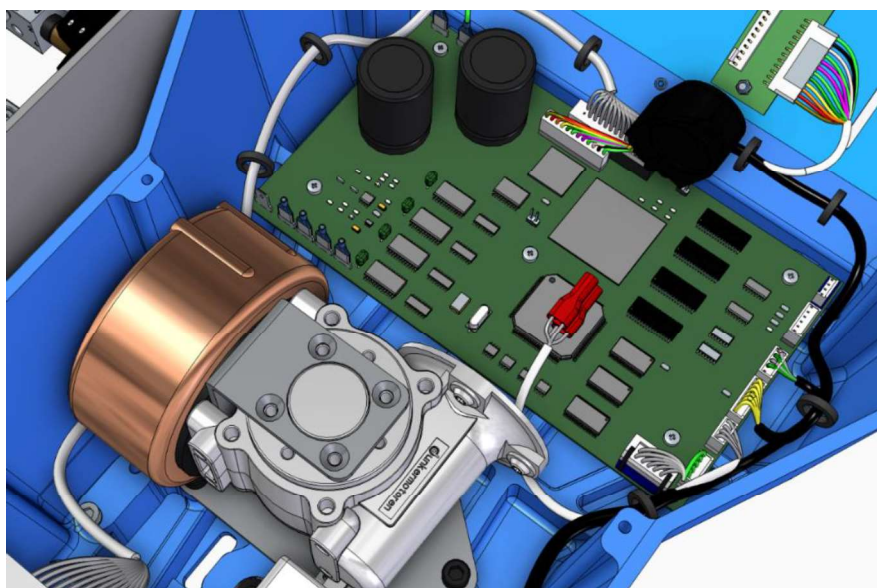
Exemplo de desenho de um PCB. (*Solid Edge*, 2019)
